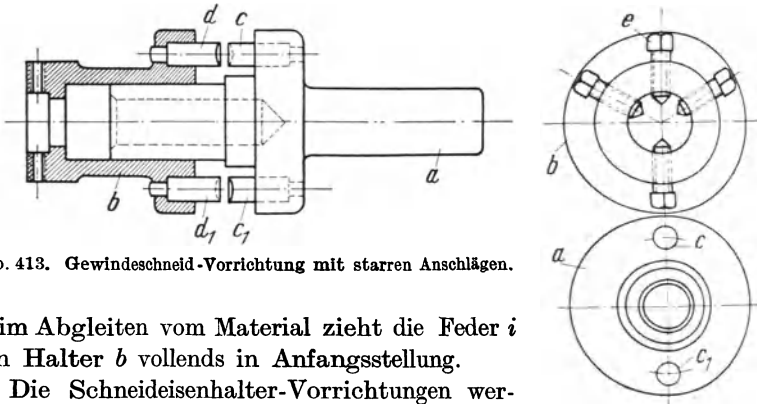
Gewindeschneid-Vorrichtung mit starren Anschlägen.
